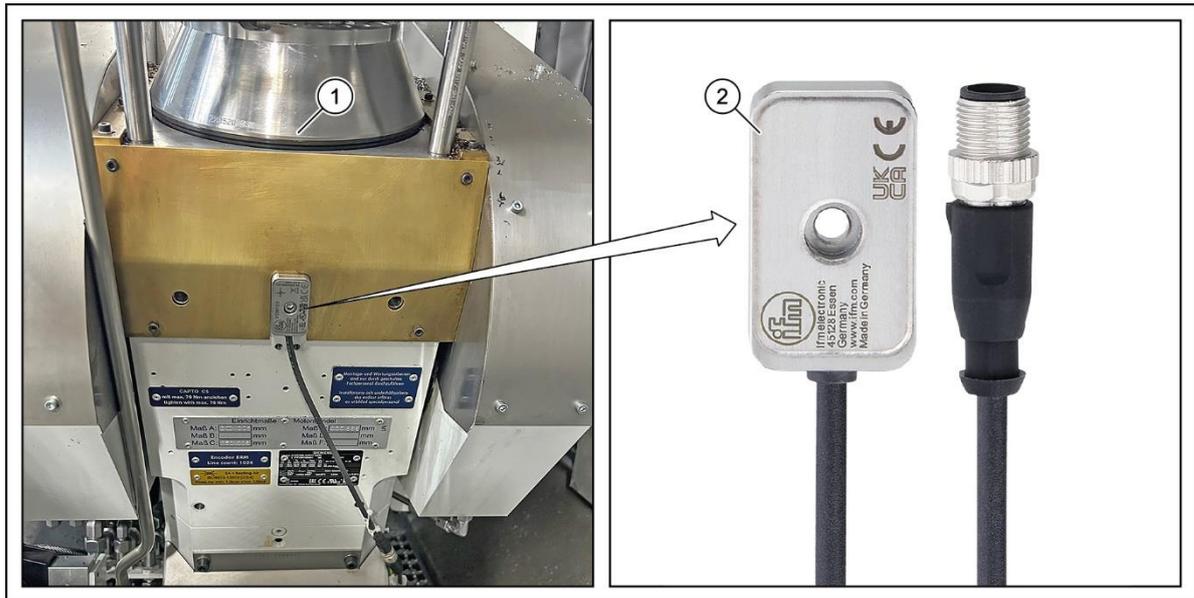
Dreiachsiger Schwingungssensor an den Werkzeugspindeln - SynchroForm
